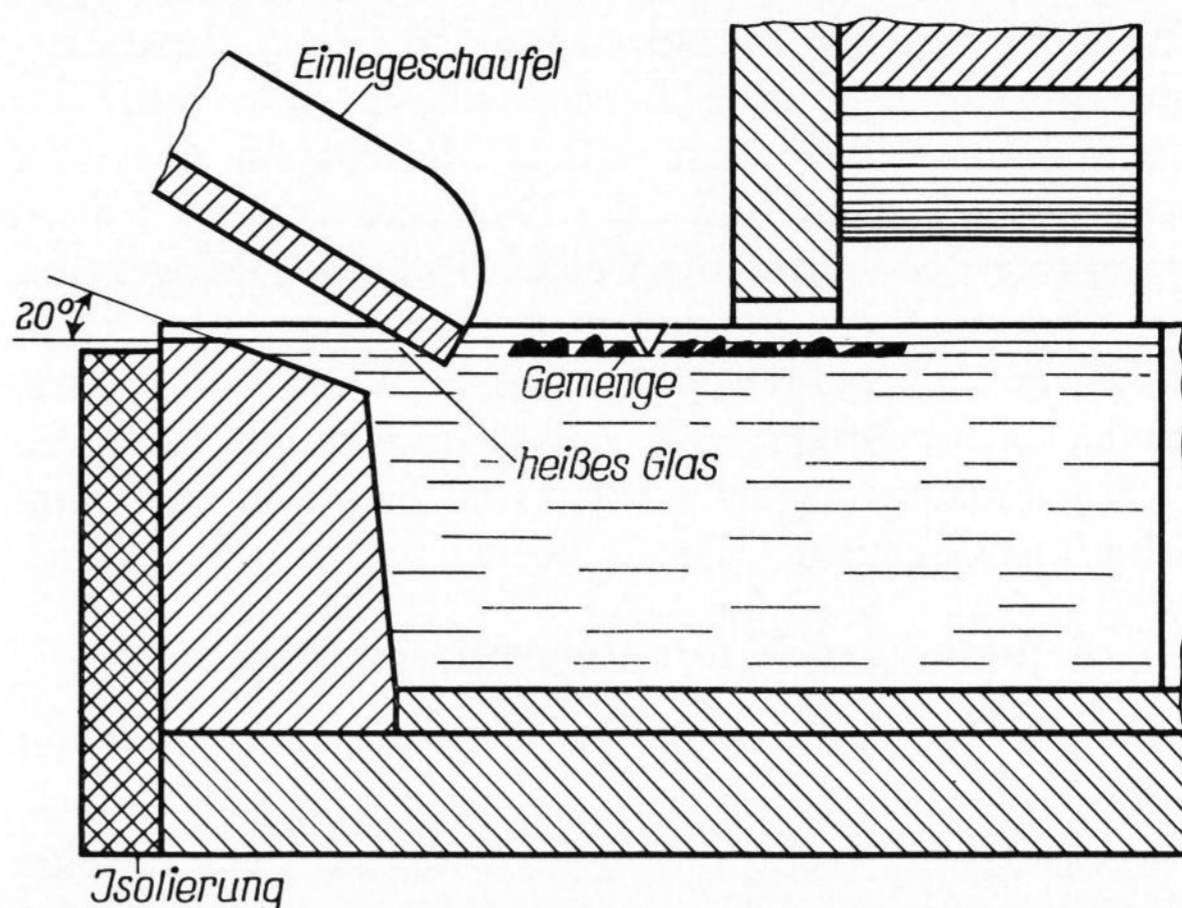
Einlegevorbau mit doppelt abgeschrägtem Stein an der Stirnwand.
